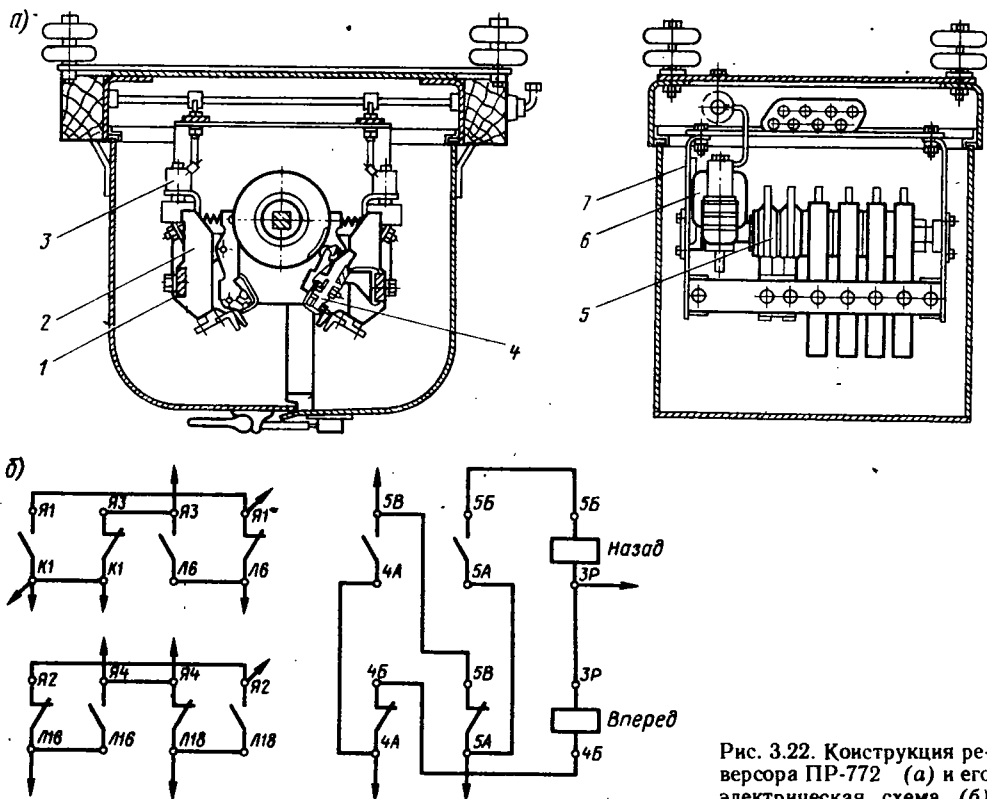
Конструкция реверсора ПР-772 (а) и его электрическая схема (б)
